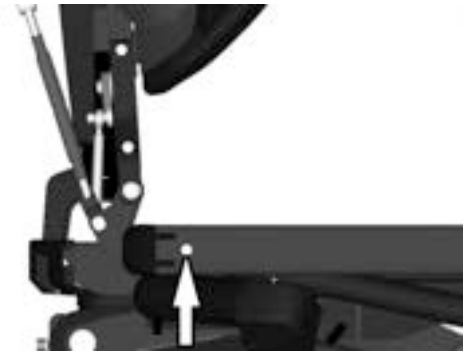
Hintere Befestigungsschraube der UniTrack-Schiene.
